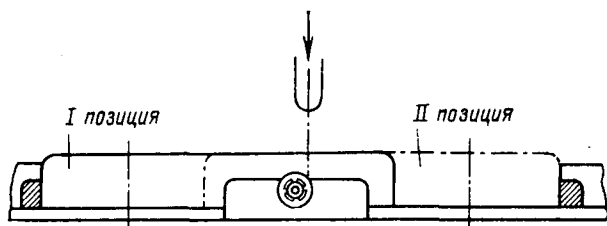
Выборка в заготовке двух гнезд на цепнодолбежном станке
